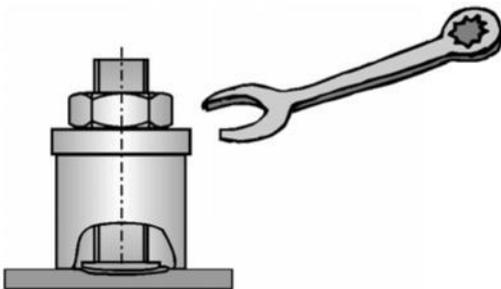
Zugprüfung einer Bolzenschweißverbindung
